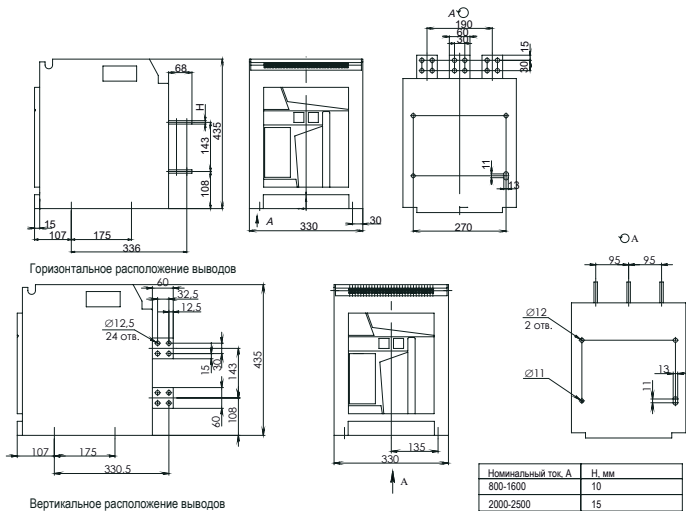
Габаритные размеры выдвижных трехполюсных выключателей типоразмера D
